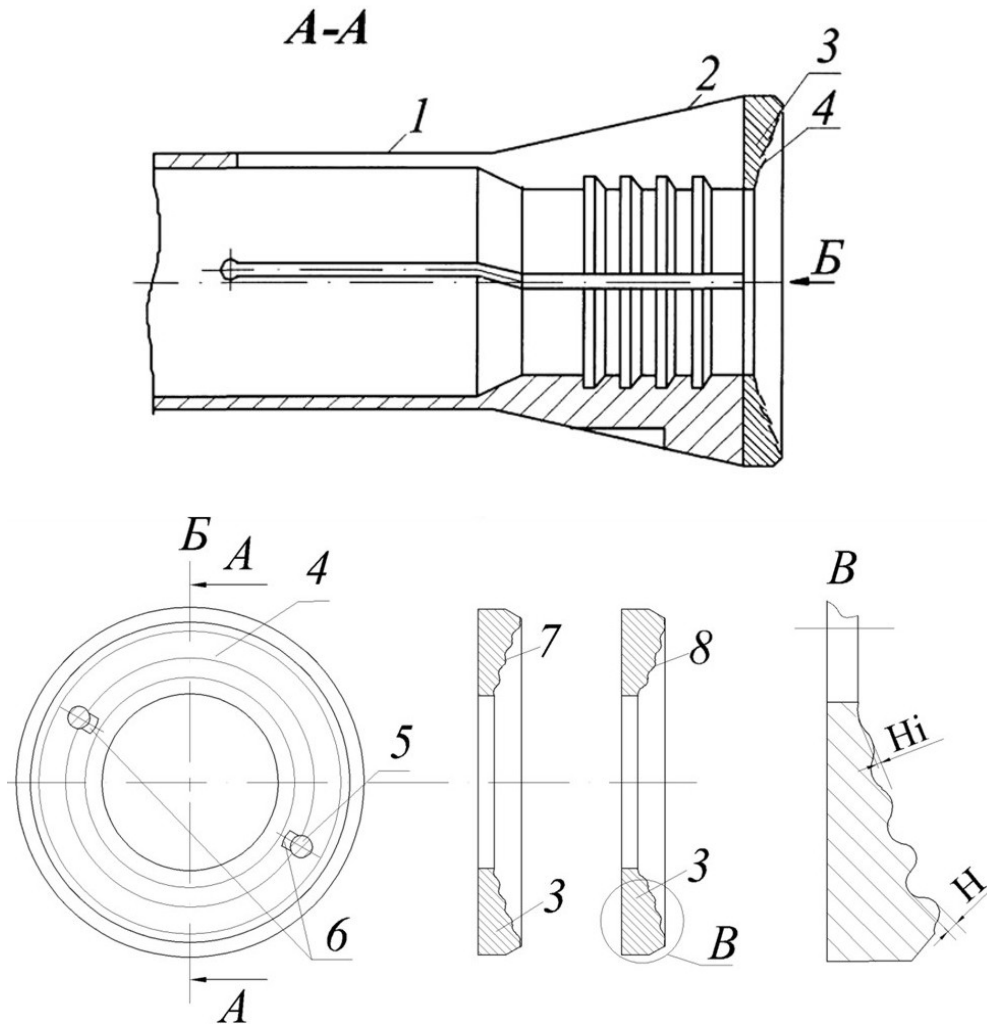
Затискна цанга з підвищеною надійністю для затиску заготовок: 1 – пружна частина, 2 – робоча кінцева частина, 3 – кришка з криволінійними 4 твірними вгнутої 7 та опуклої 8 форми, 5 – гвинти, 6 – пази
